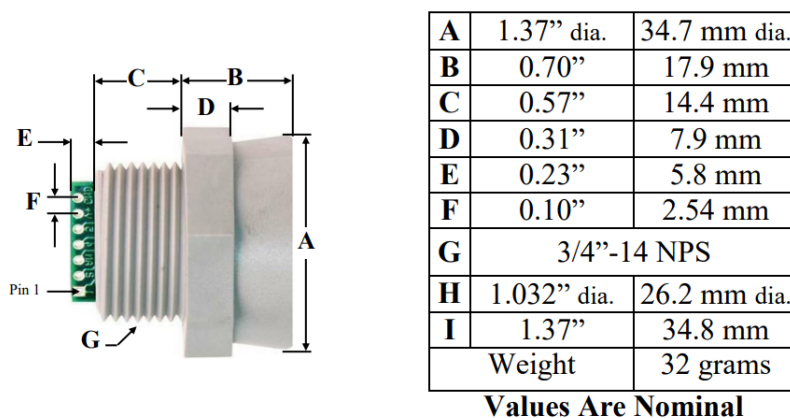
Sensor RADAR - Modelo MB7062 XL-MaxSonar-WR1 – Dimensões, [38]
